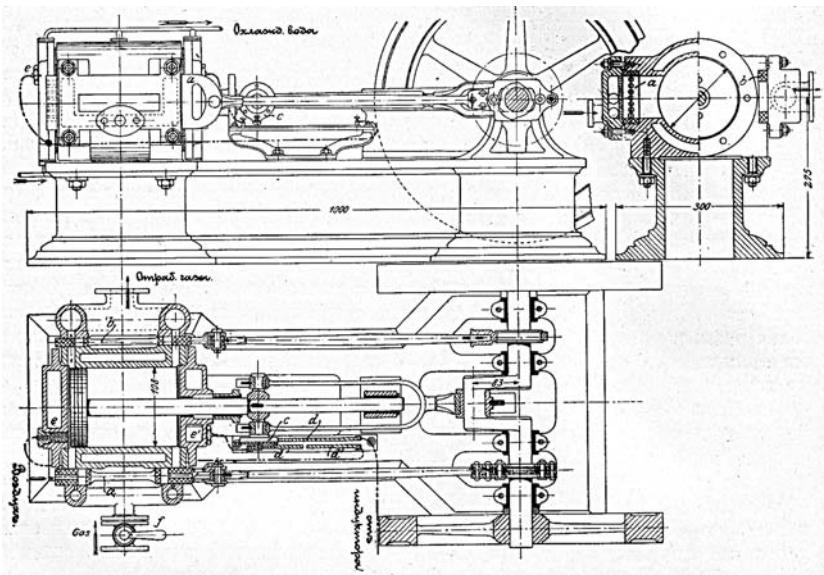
Горизонтальный газовый двигатель двойного действия Ленуара.
